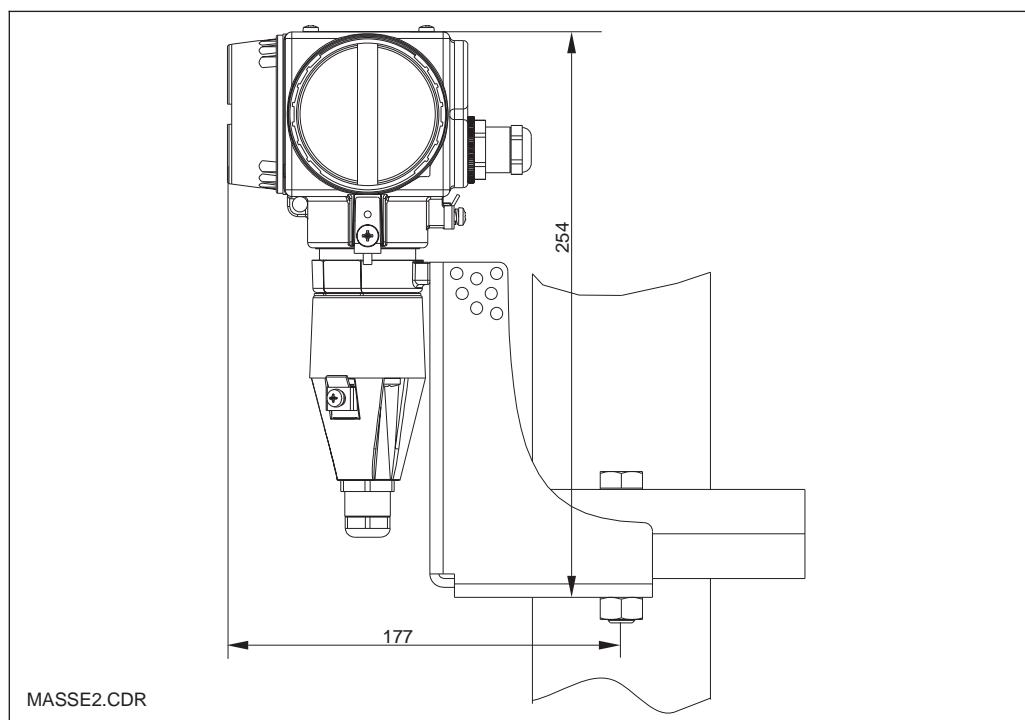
Montage am Flansch mit Befestigungswinkel
